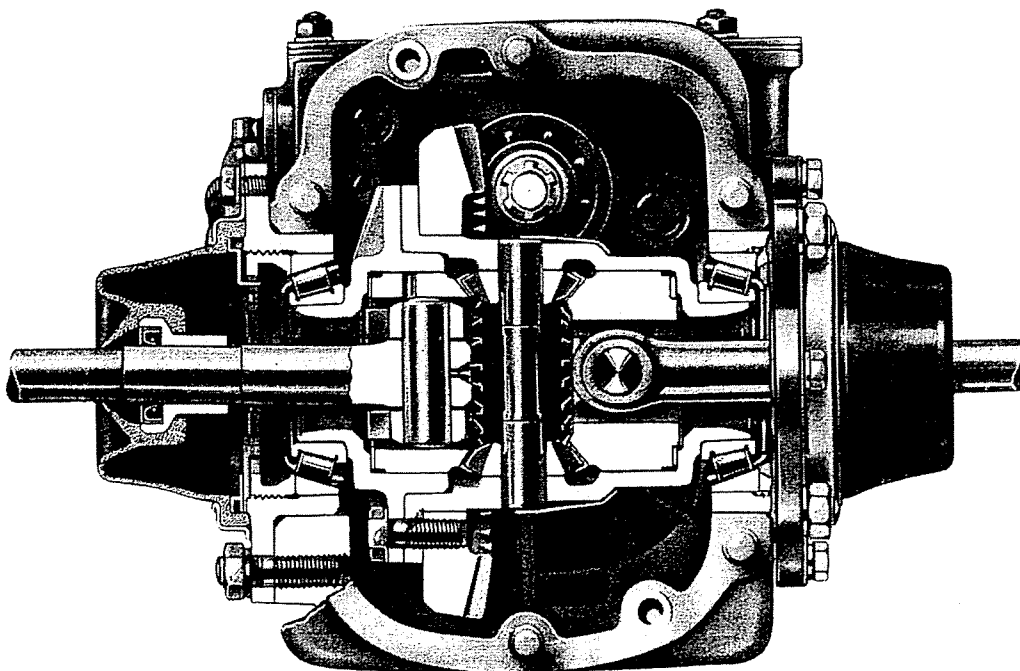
Querschnitt des Ausgleichgetriebes durch die Hinterachswellen.
